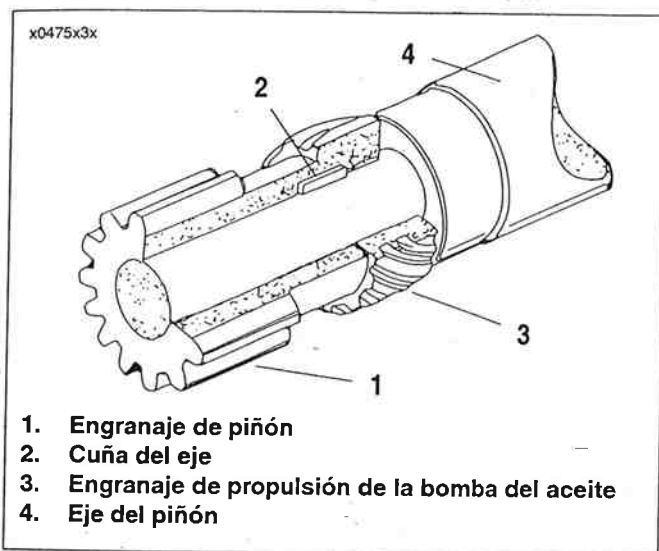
Engranaje de propulsión de la bomba de aceite y engranaje de piñón instalados en el eje del piñón
